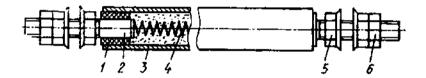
Трубчатый электронагреватель: 1 – изолятор; 2 – выводной стержень; 3 – корпус; 4 – нихромовая спираль; 5, 6 – клеммные гайки
